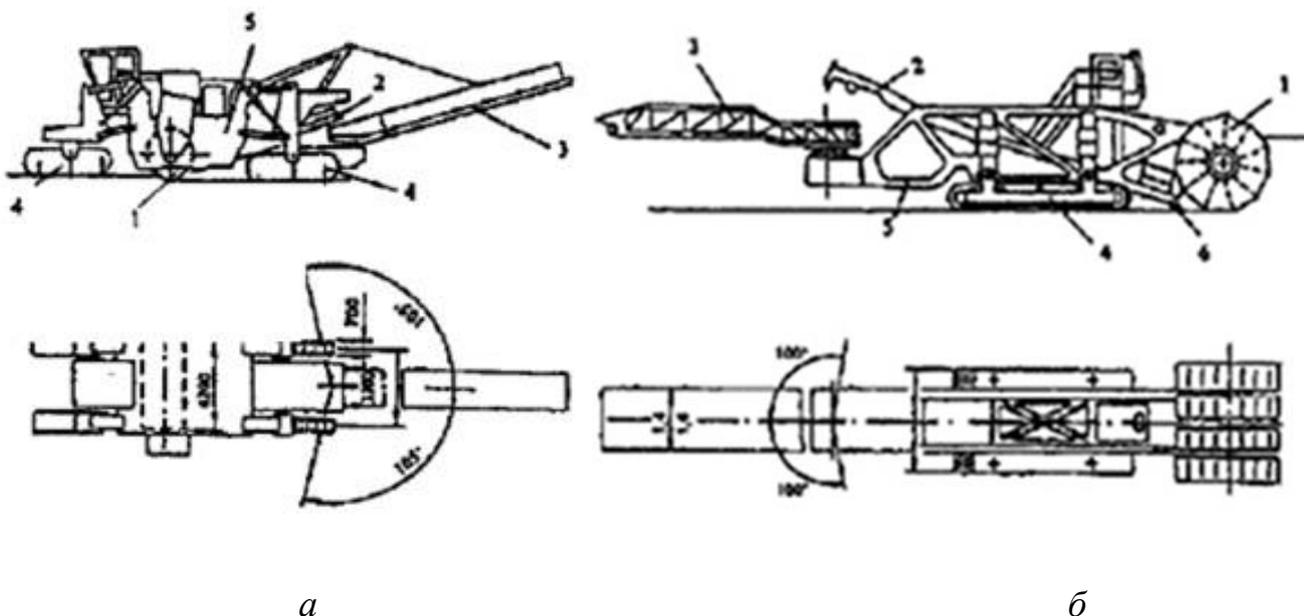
Конструктивная схема экскаватора продольного черпания фрезерного типа СМ: а — комбайн фирмы «Виртген»; б — комбайн фирмы «Крупп» машины
